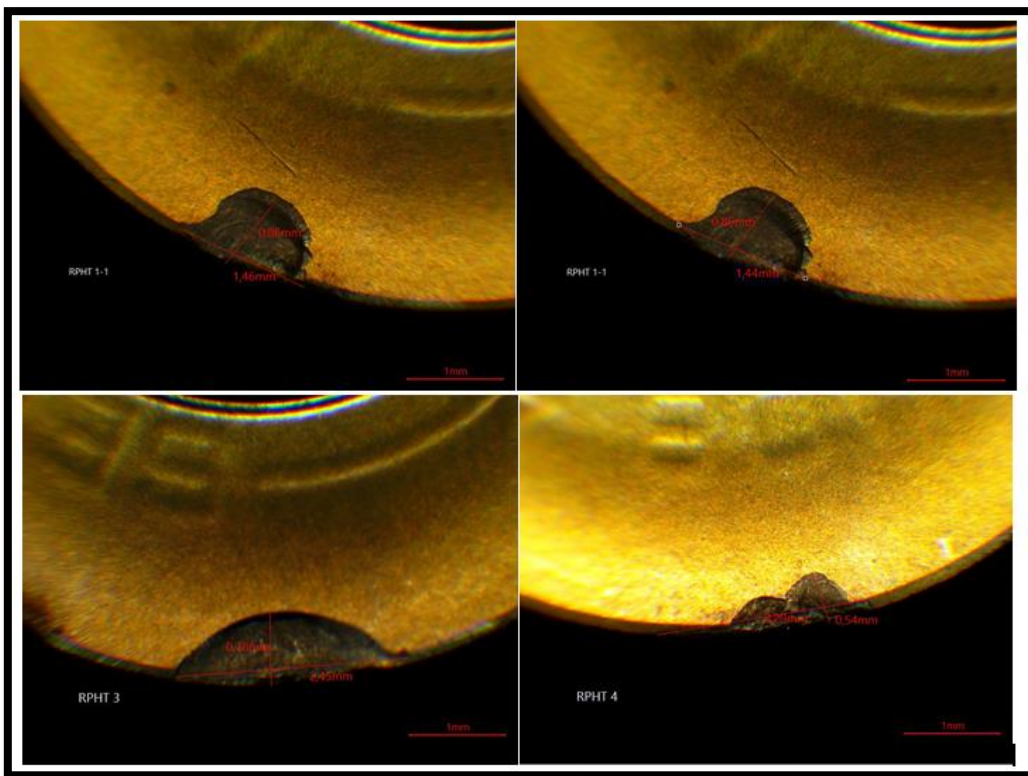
Observation microscopique de l'usure en cratère fracture sur les faces de coupe des plaquettes type RPHT revêtue.
